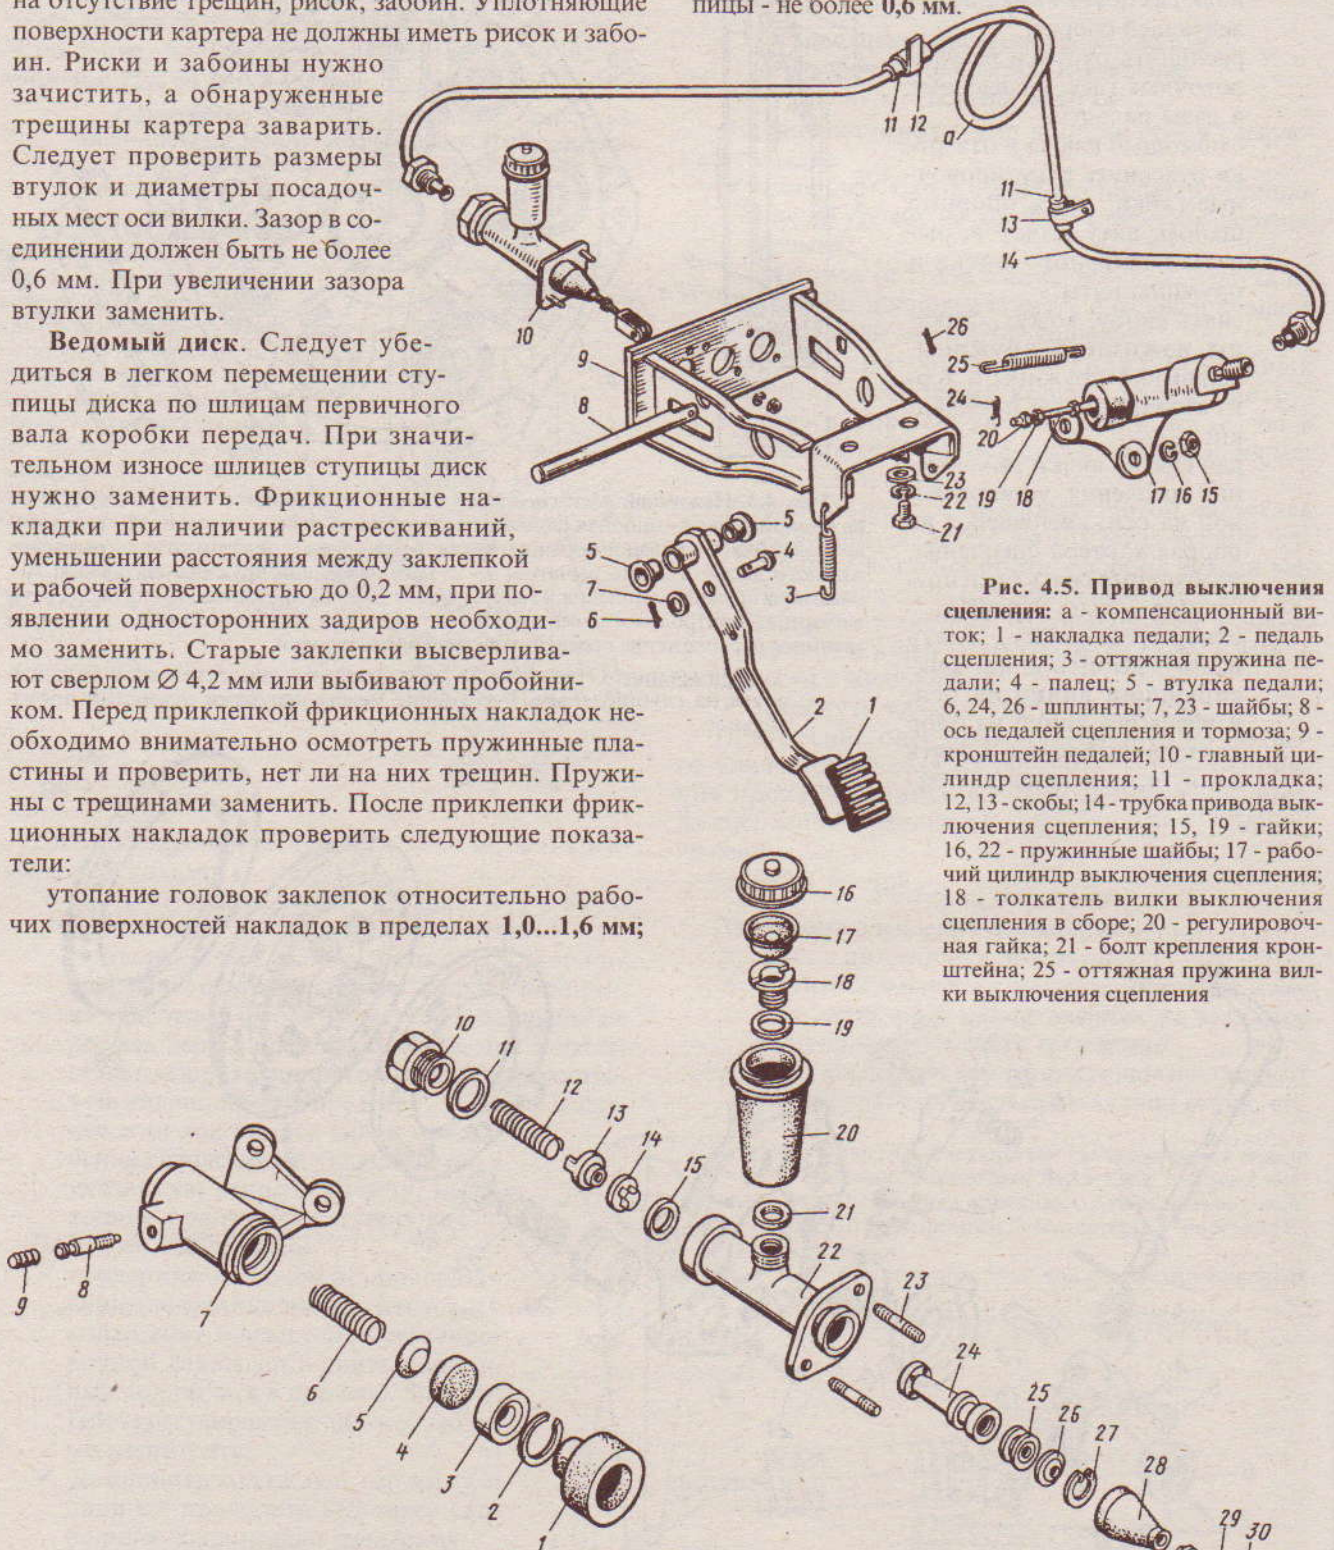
Привод выключения сцепления: а - компенсационный виток; 1 - накладка педали; 2 - педаль сцепления; 3 - оттяжная пружина педали; 4 - палец; 5 - втулка педали; 6, 24, 26 - шпильки; 7, 23 - шайбы; 8 - ось педалей сцепления и тормоза; 9 - кронштейн педалей; 10 - главный цилиндр сцепления; 11 - прокладка; 12, 13 - скобы; 14 - трубка привода выключения сцепления; 15, 19 - гайки; 16, 22 - пружинные шайбы; 17 - рабочий цилиндр выключения сцепления; 18 - толкатель вилки выключения сцепления в сборе; 20 - регулировочная гайка; 21 - болт крепления кронштейна; 25 - оттяжная пружина вилки выключения сцепления
